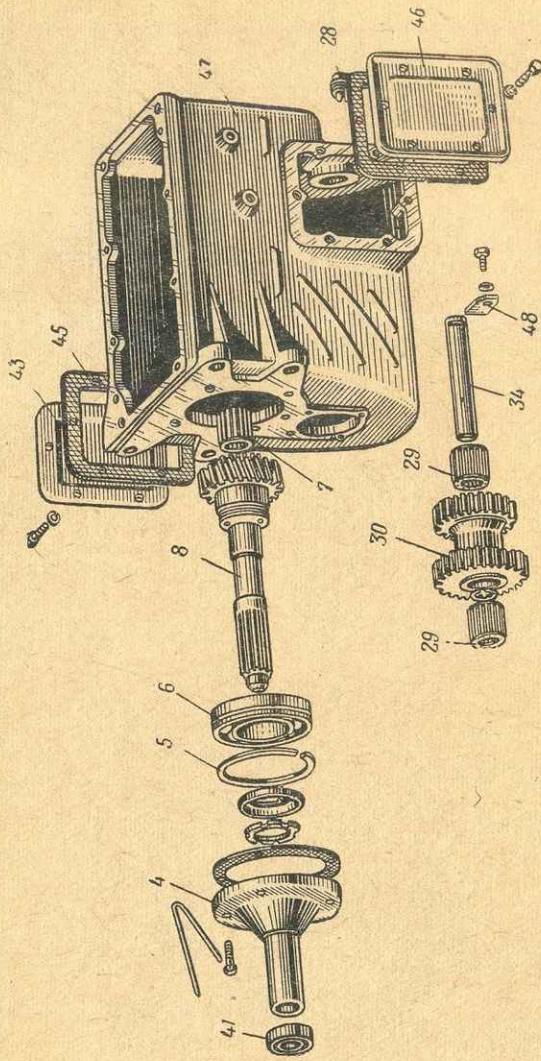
Картр, первый вал, шестерня заднего хода (обозначения деталей те же, что и на рис. 52)
